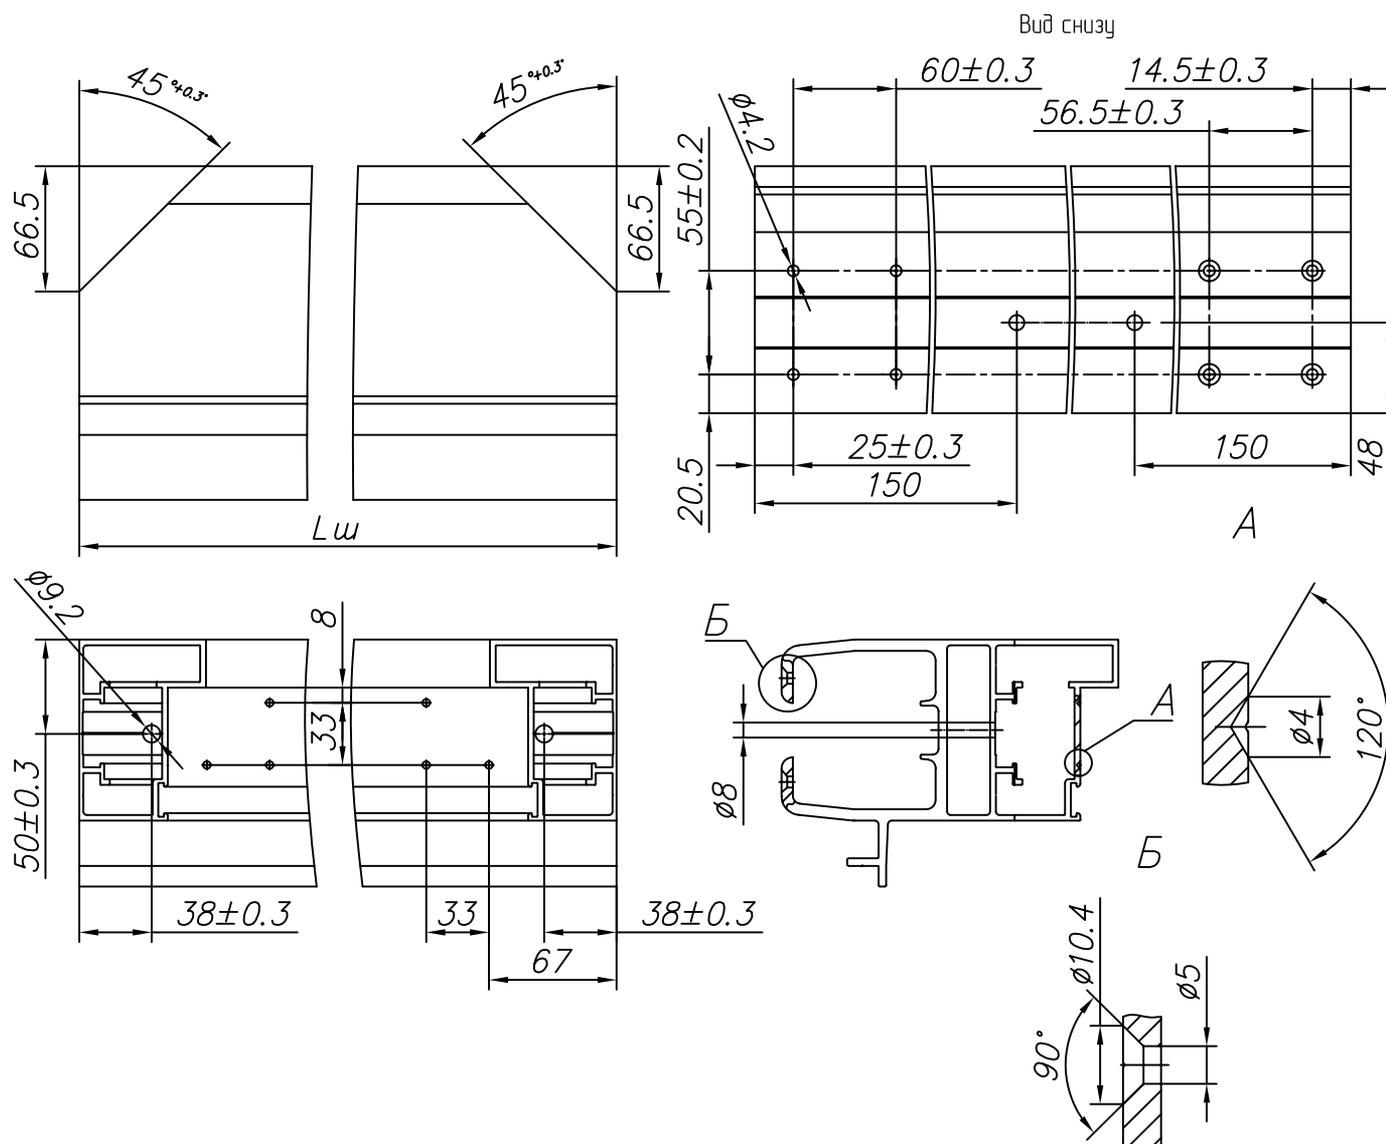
Изготовление штыря для пассивной(опорной) створки (открывание вправо)
